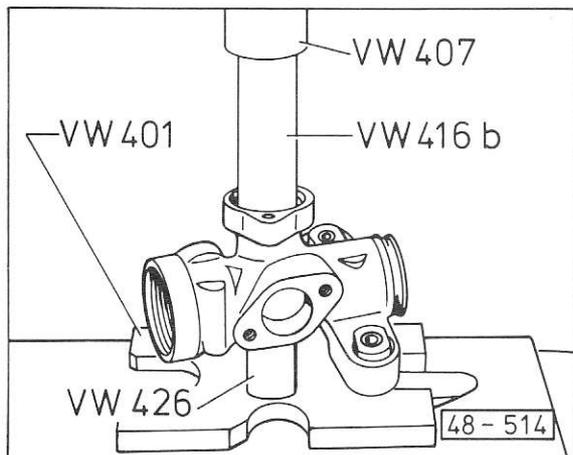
Bague-joint: emmanchement sur le boîtier de pignon
